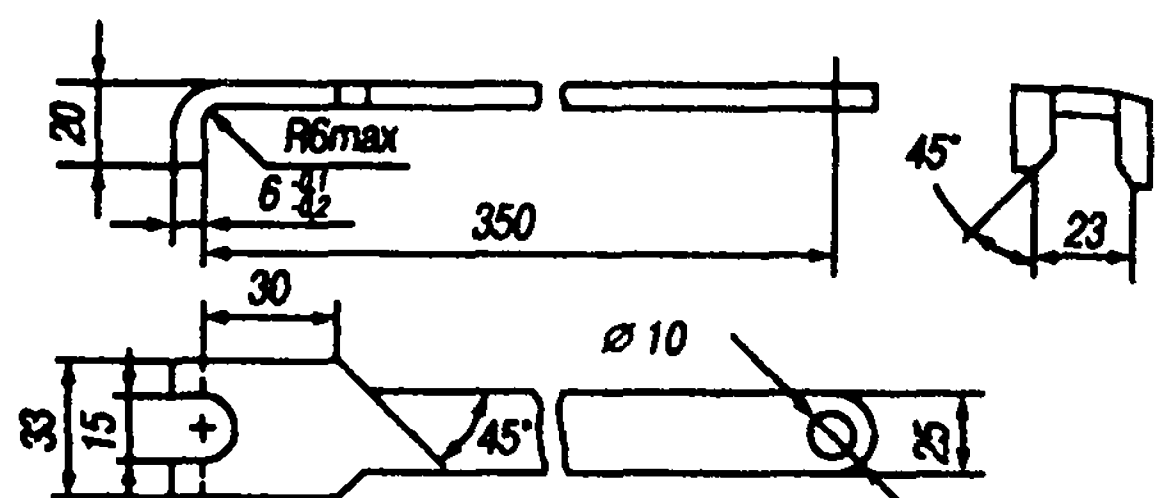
Специальный ключ для отвертывания гайки резервуара
